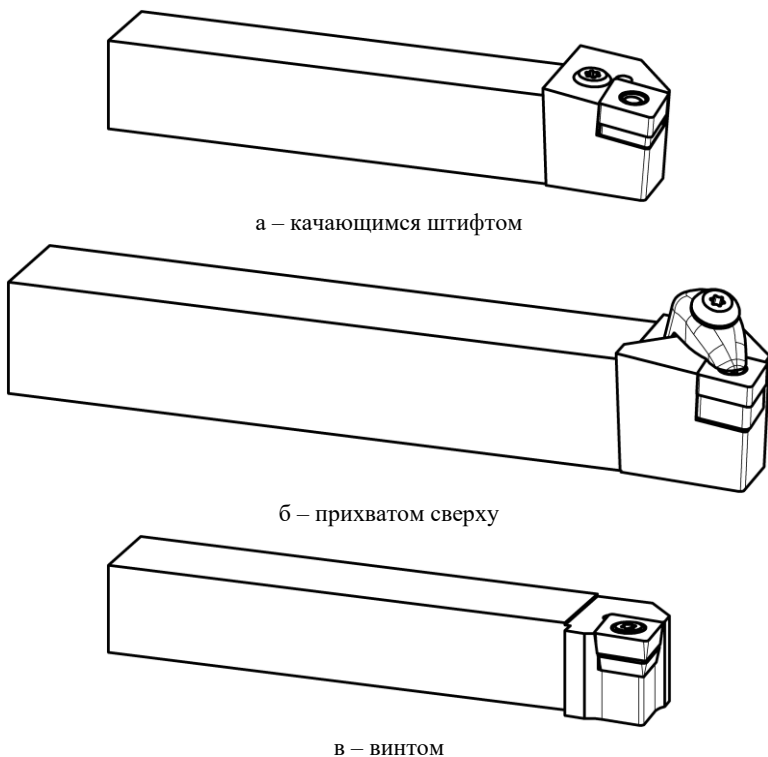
Примеры державок с различным креплением пластины формы С
